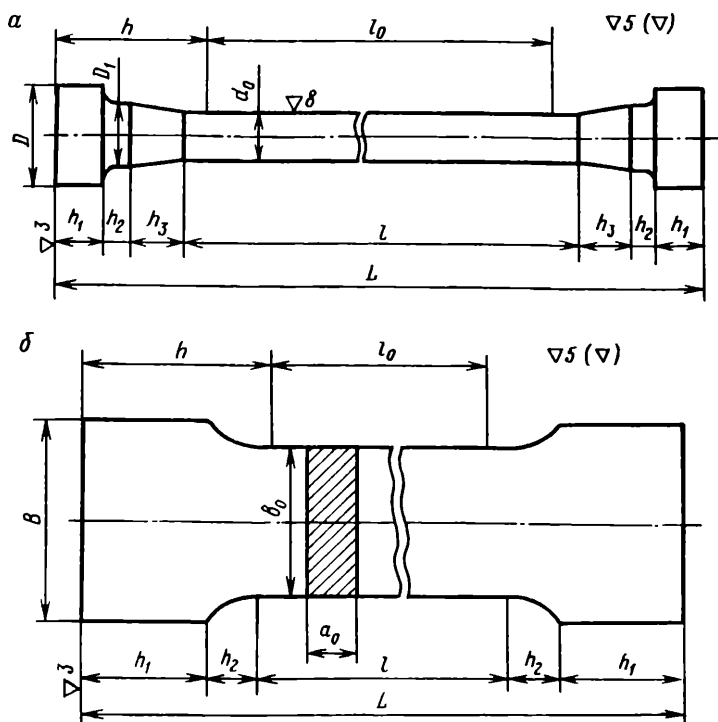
Образцы для испытания типа I цилиндрический (а) и плоский пропорциональный (б):
